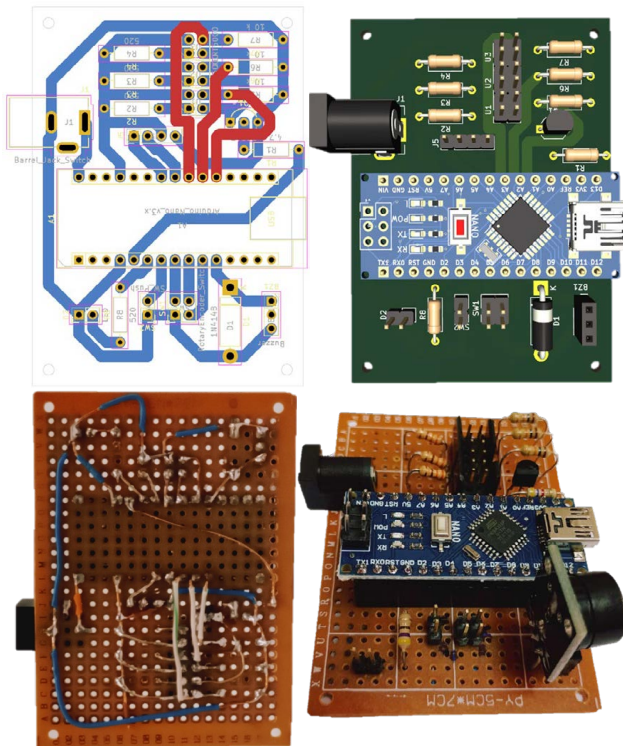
Arriba: Diseño de circuito. Abajo: Circuito soldado en placa experimental perforada.
